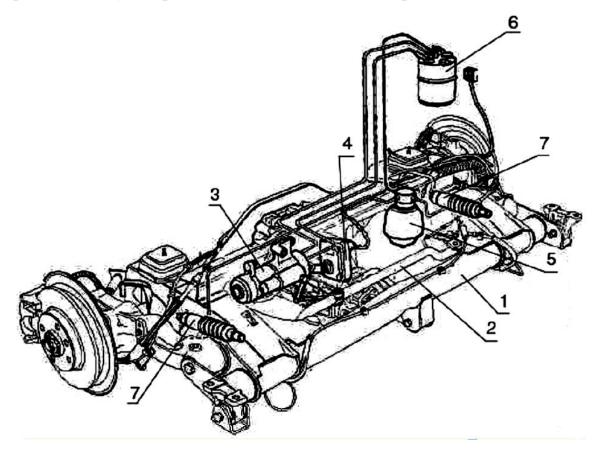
Гидропневматическая подвеска с изменяемым дорожным просветом: 1 — поперечная балка; 2 — торсион; 3 — насос; 4 — датчик высоты кузова; 5 — бачок-гидроаккумулятор с азотом; 6 — заливной бачок; 7 — гидроцилиндры подвески
